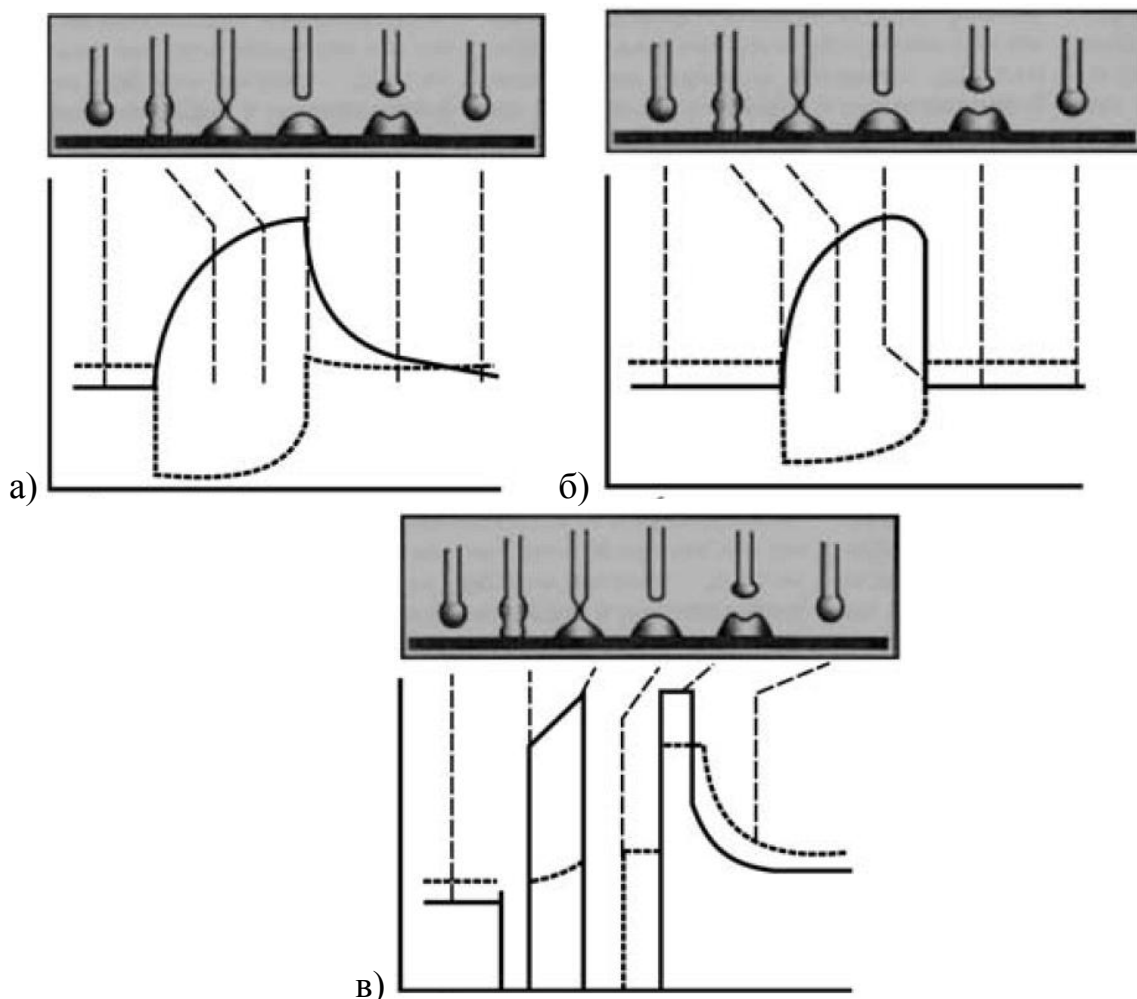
Типичные формы кривых сварочного тока (—) и напряжения (- - -) при традиционной сварке в углекислом газе (а), при сварке с ВКЗ (б) и при STT процессе (в) [15].
